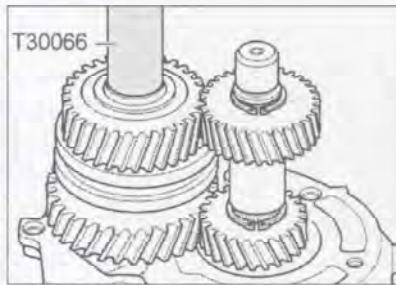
Нагрев внутреннюю обойму подшипника первичного вала до 100°C, напрессуйте ее до упора на вал.
